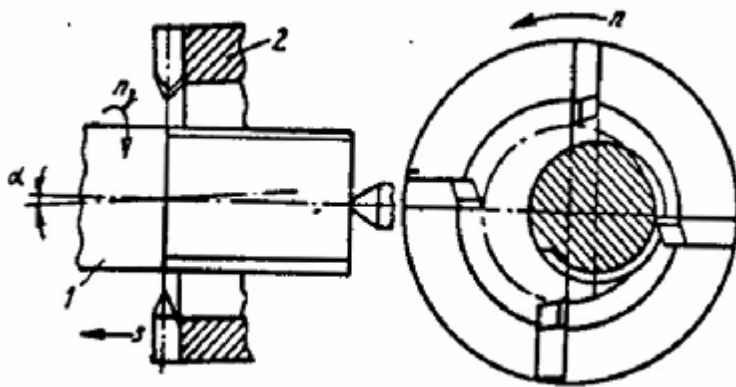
Схема вихревого фрезерования резьбы (подача S равна шагу резьбы)
